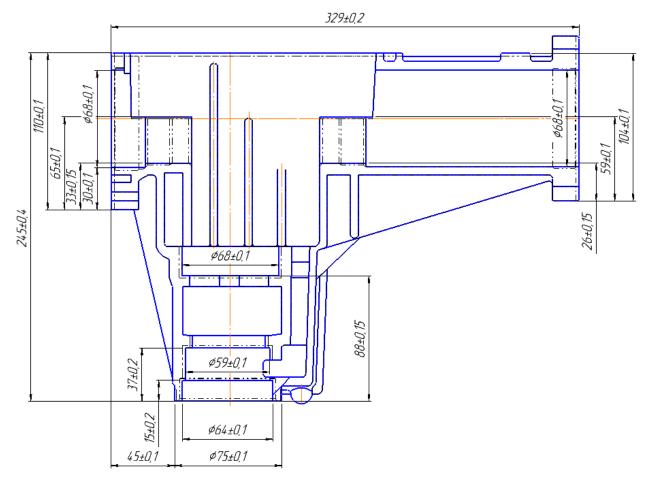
Заготовка полученная методом литья в металлическую форму под давлением
